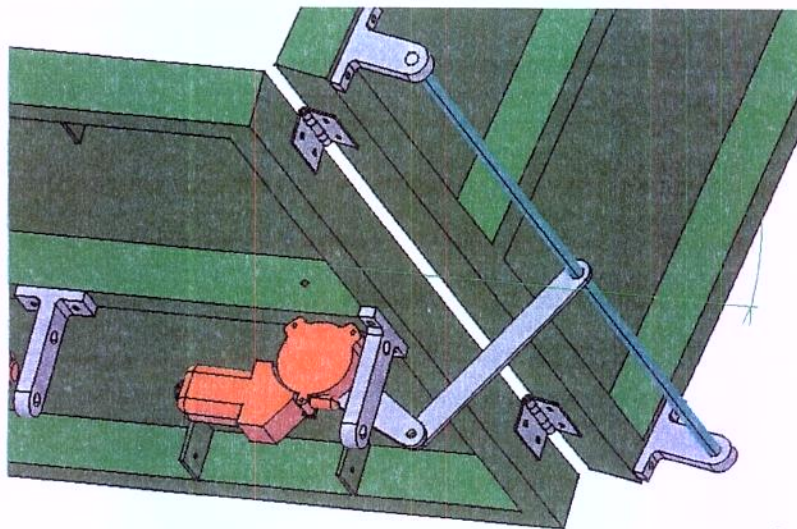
Detalhe do acionamento do apoio do tronco.
